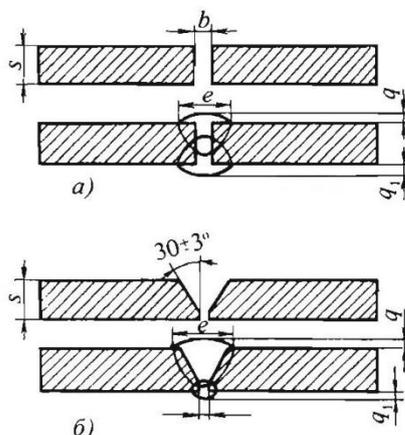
Основные конструктивные элементы сварных швов: а - без подготовки кромок малых толщин (b - ширина зазора); б - с V-образной разделкой
